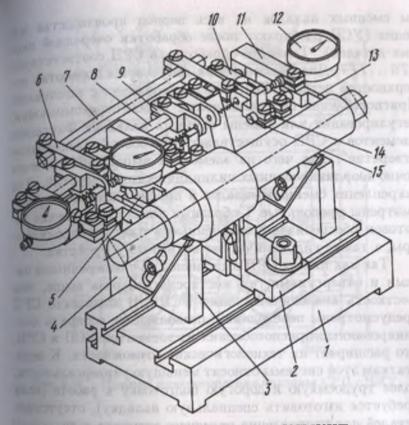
Пример компоновки УСМКИП: 1 – плита; 2 – планка суппорта; 3 – призма; 4 – державка; 5, 13 – упоры; 6 – планка; 7, 8, 15 – валики; 9, 10, 14 – зажимные планки; 11 – державка; 12 – индикатор
